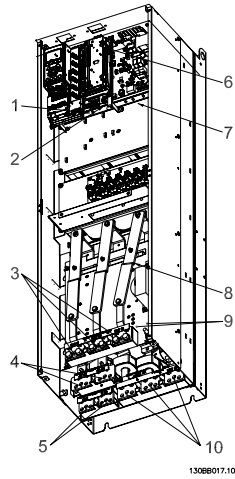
Kompaktgeräte IP00 (Chassis), Baugröße D3
